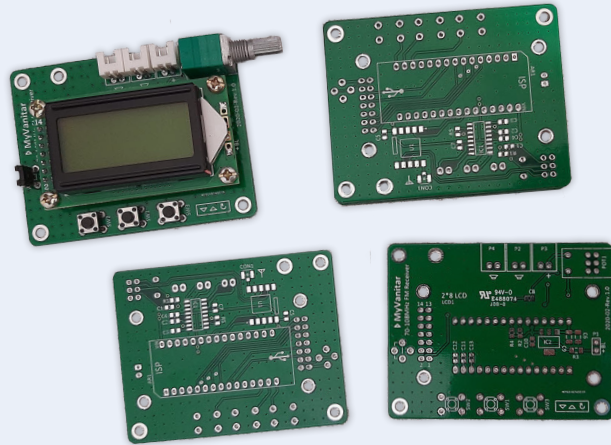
Carte assemblée (vue de dessus) et nue (3 vues).
